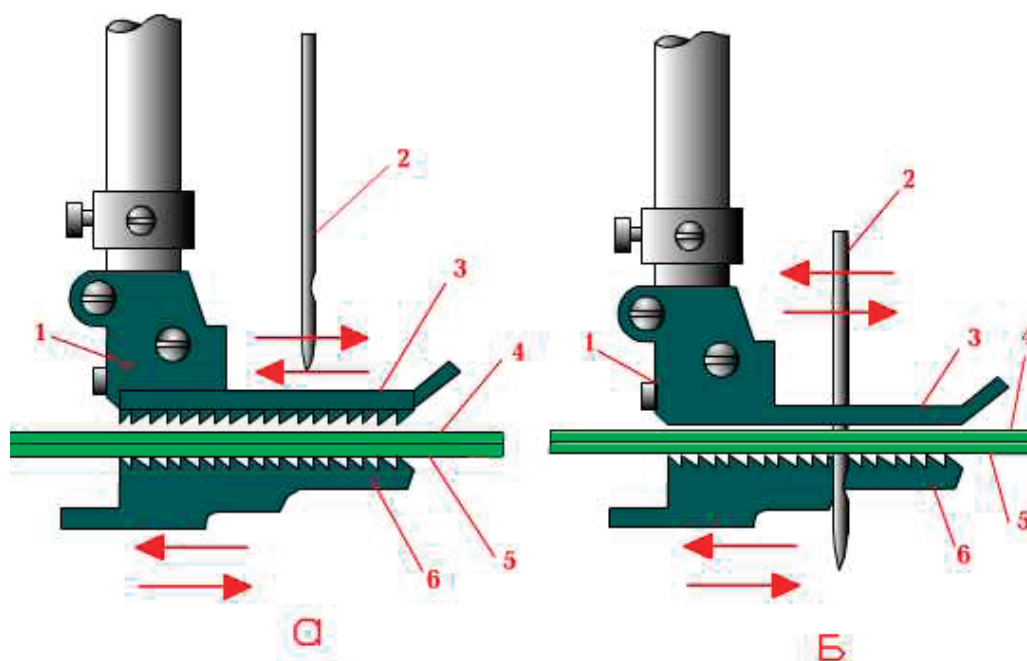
Механизм перемещения материала при помощи иглы и зубчатой рейки.
